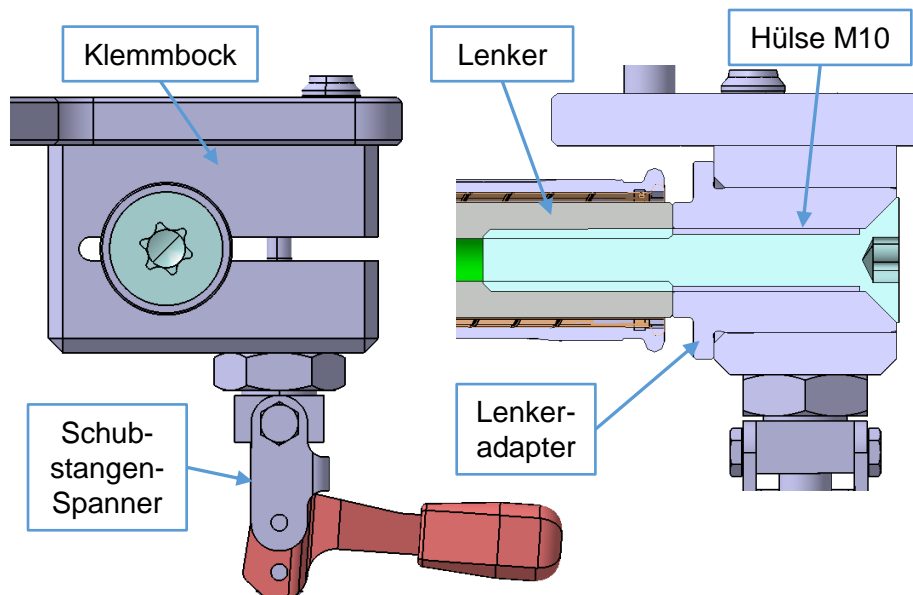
Modul MV1 – Komponenten zur Montage der vorderen Messeinrichtung am Lenker mittels kraftschlüssiger Klemmverbindung mit Lenkeradapter, Hebelnabe (Klemmbock) und Schubstangen-Spanner. Hülse zur Anpassung an Lenker mit M10 Gewinde.
